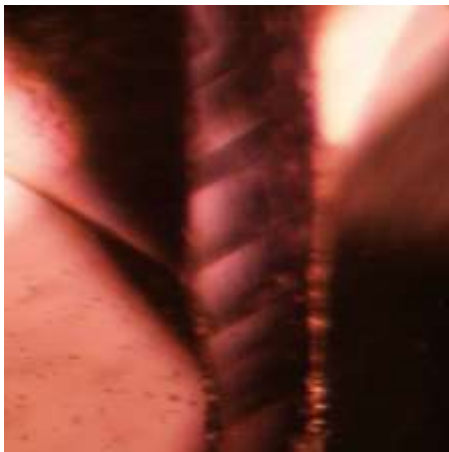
CV28 on aperçoit les LP sur le rondiste
